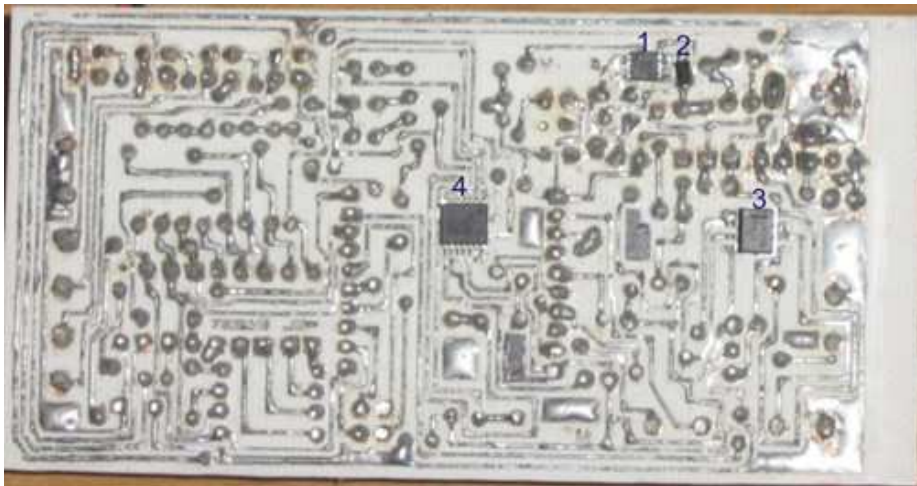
Vista del lado soldadura del XBeeSensor.
